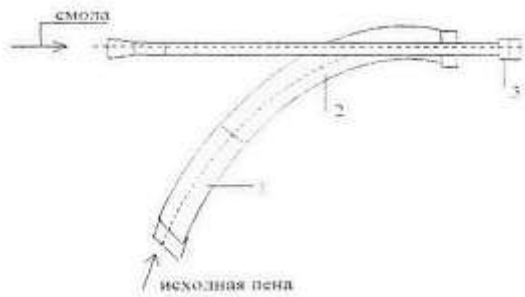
Схема змішувача: 1 - корпус; 2 - труба для подачі смоли; 3 - форсунка.
